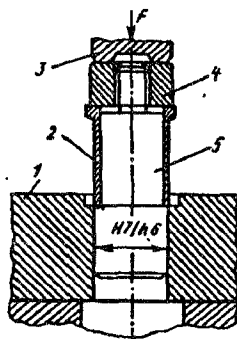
Схема получения неразъемного неподвижного соединения диска с втулкой
